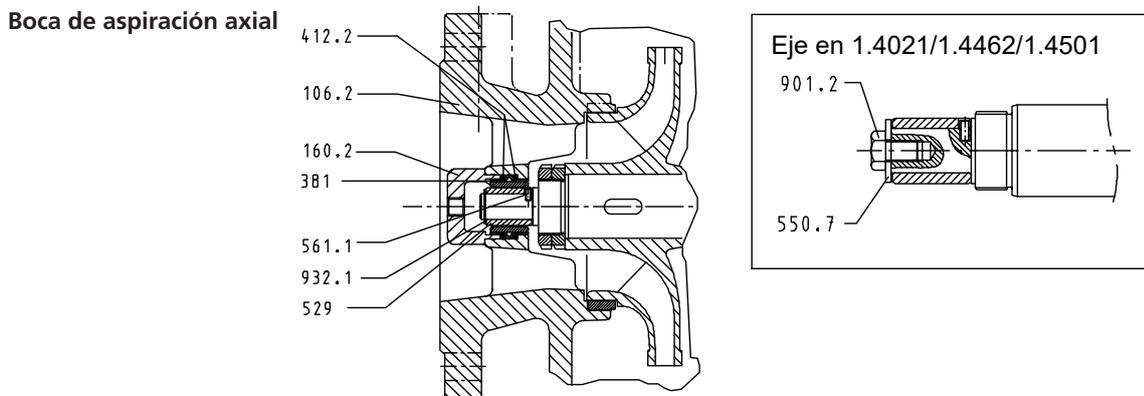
Desmontaje del cojinete liso: boca de aspiración axial
